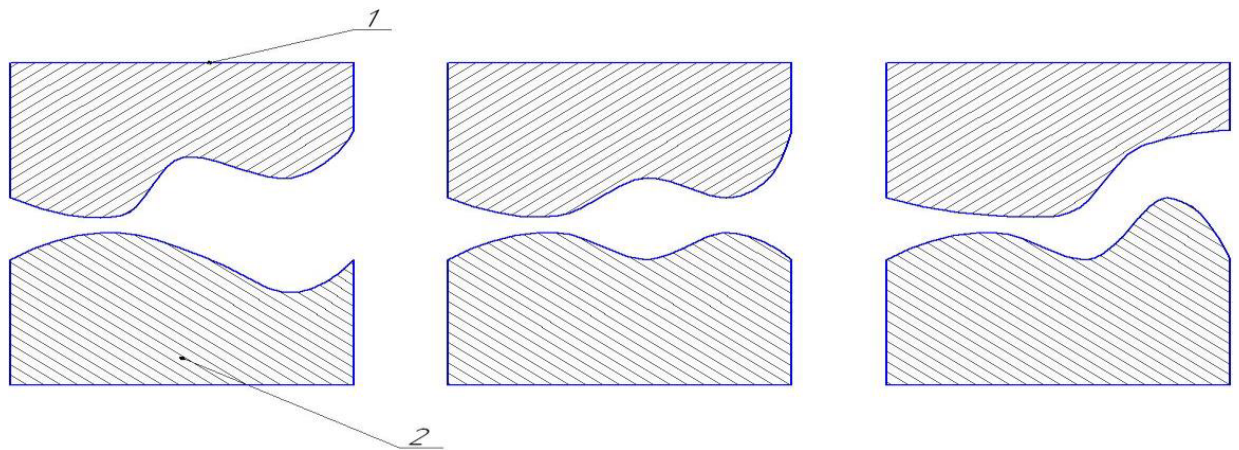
Варіанти розташування мікронерівностей западини і виступу між робочими поверхнями голки і корпусу розпилювача форсунки: 1 - корпус; 2 - голка.
